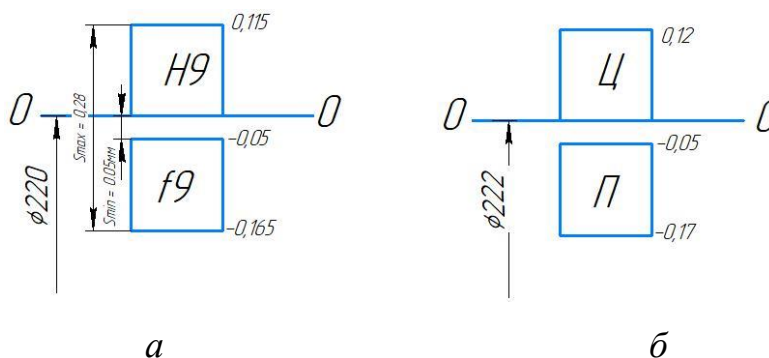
Поля допусков для отверстия в цилиндре и поршня новых деталей (а) и при переводе в ремонтный размер (б). Ц-цилиндр, П-поршень.
